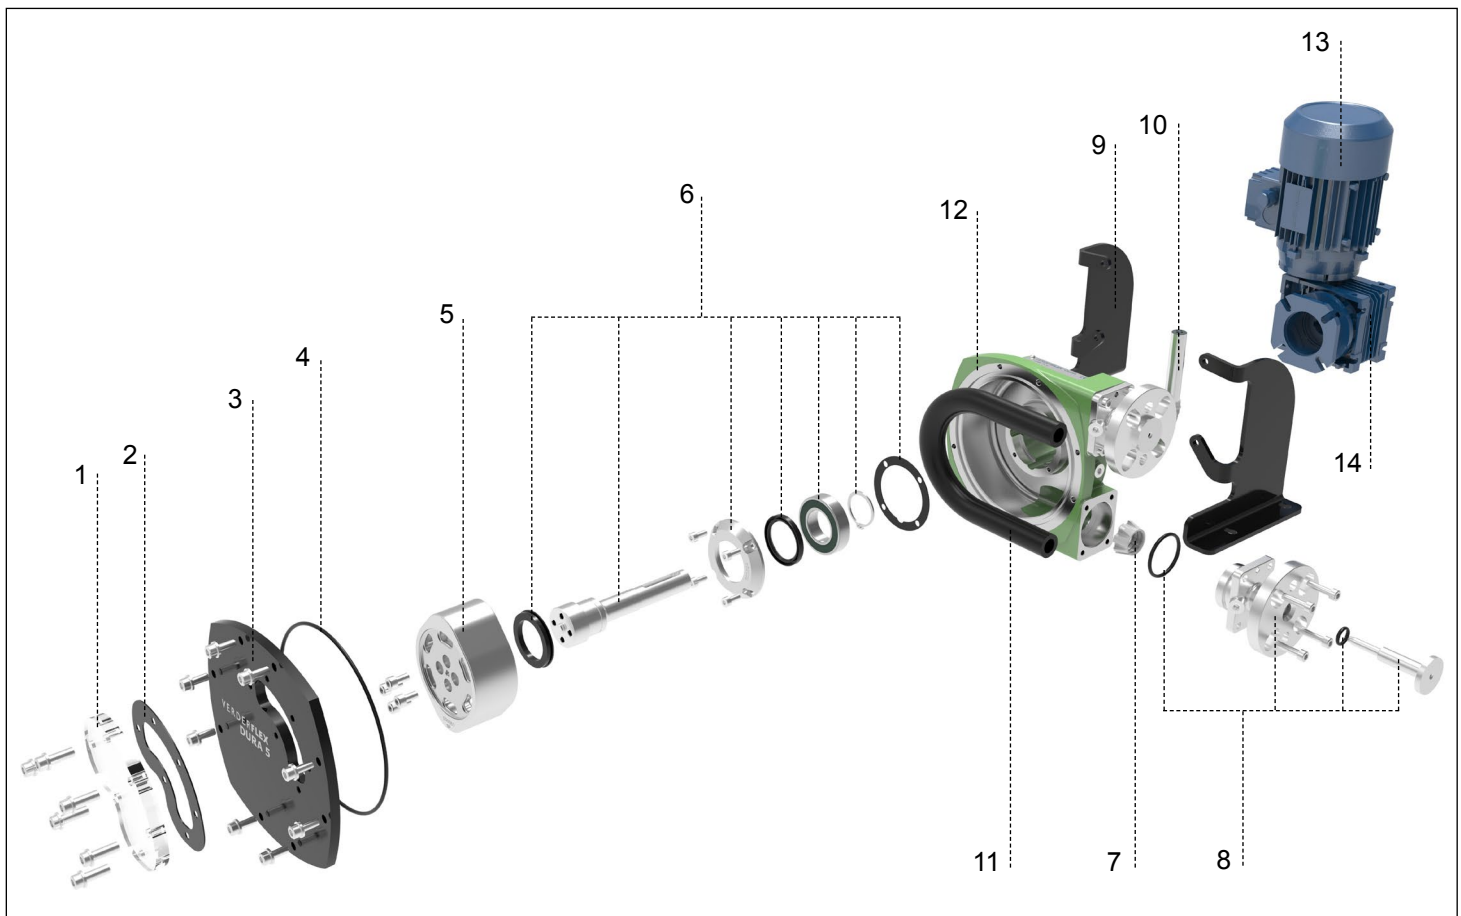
Dura MK IV 5 et 7 Vue Éclatée (Vue Générique)
